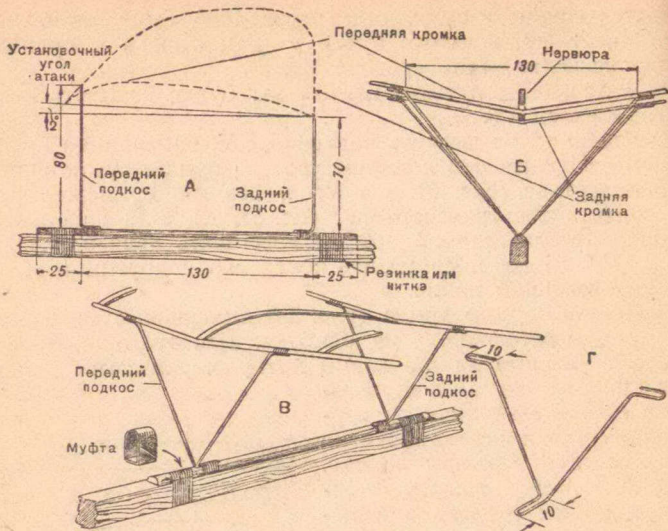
Крепление крыла: А — вид сбоку, Б — вид спереди, В — общий вид крепления крыла, Г — подкос.
